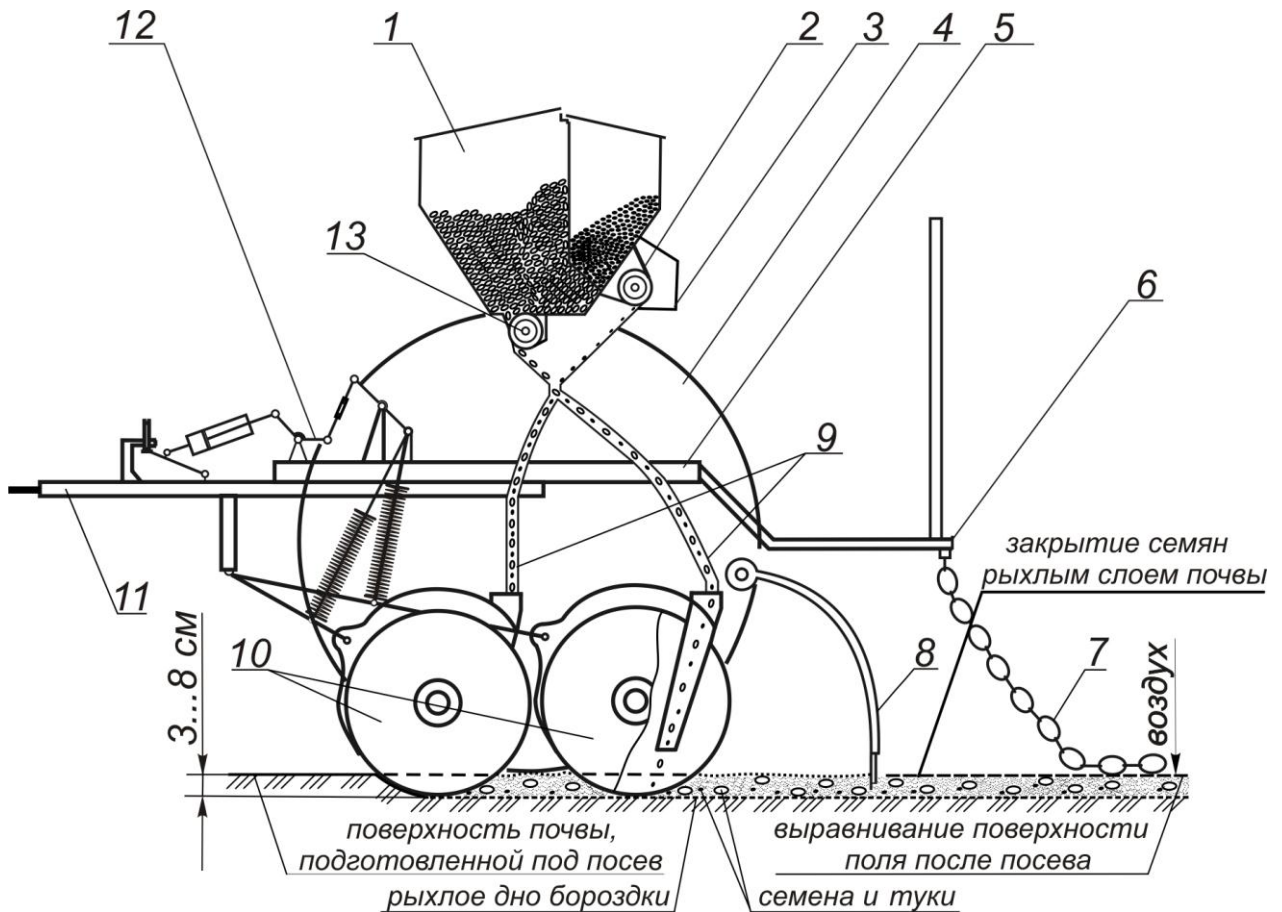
Технологическая схема зерновой сеялки СЗ-3,6 с серийными сошниками: 1 – зернотуковый ящик; 2 – туковысевающий аппарат; 3 – механизм передачи; 4 – опорно-приводные колеса; 5 – рама; 6 – подножная доска; 7 – цепной шлейф; 8 – загортачи; 9 – семяпроводы; 10 – двухдисковые сошники; 11 – прицепное устройство; 12 – механизм подъема и опускания сошников; 13 – семявысевающий аппарат; 14 – прижимная пластина
